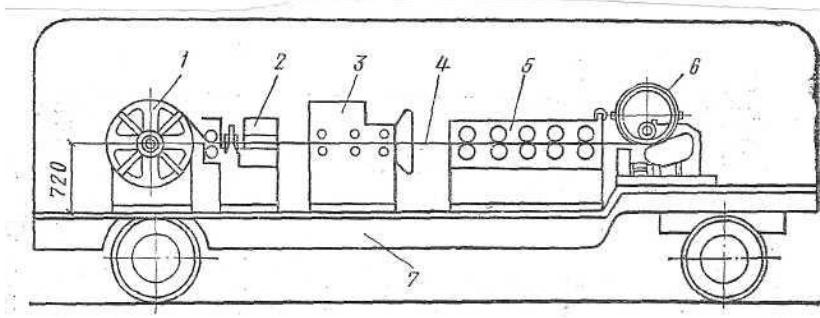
Схема передвижной установки для изготовления спирально-замковых воздуховодов
